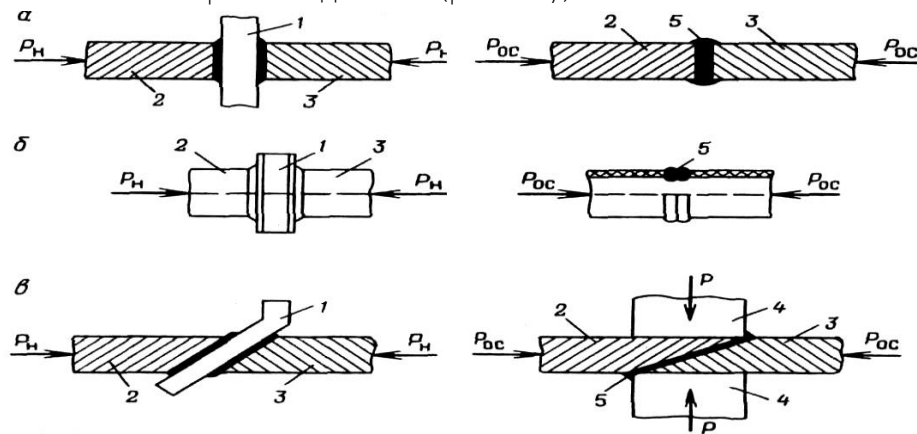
Схемы сварки нагретым инструментом прямым нагревом:
